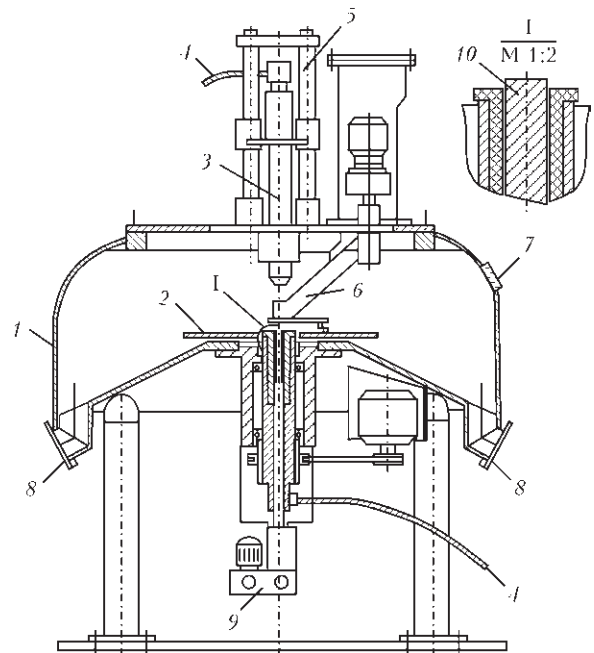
Схема установки для распыления слитков: 1 — корпус камеры; 2 — шпиндельный узел; 3 — плазматрон; 4 — токоподвод; 5 — механизм регулировки плазматрона; 6 — механизм загрузки стержня; 7 — смотровое окно; 8 — сборники готовой продукции; 9 — механизм подачи стержня; 10 — распыляемый стержень
